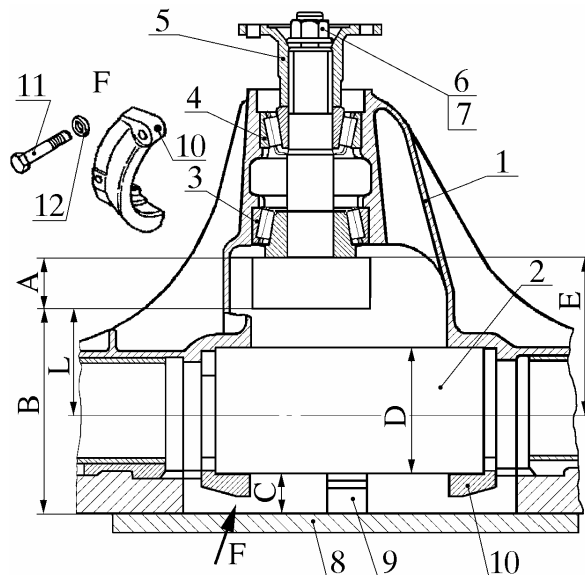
Установка специальной оправки №2 в гнезда подшипников дифференциала и определение размера С: 1 - картер с кожухами полуосей; 2 - специальная оправка №2; 3 - подшипник задний; 4 - подшипник передний; 5 - фланец ведущей шестерни; 6 - гайка; 7 - шайба; 8 - призма поверочная; 9 - концевая мера типа ГОСТ 9038-90; 10 - крышка подшипников дифференциала, дет. 3102-2403026; 11 - болт М12; 12 - шайба 12.0Т
